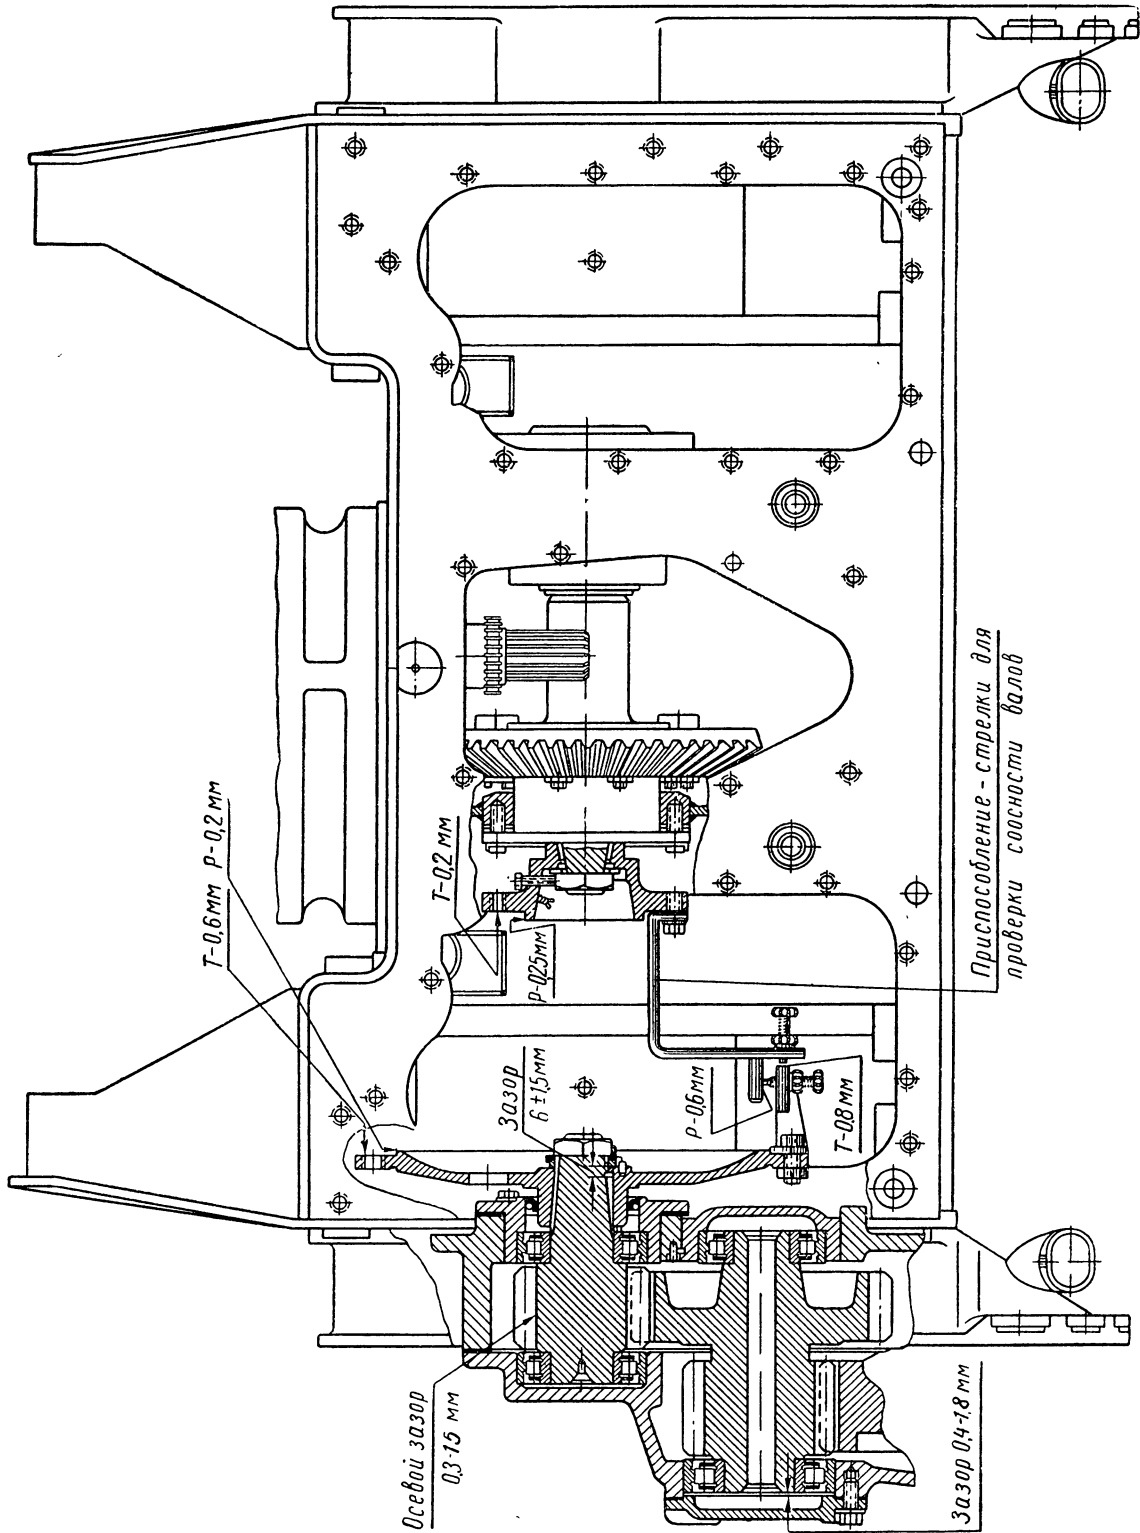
Схема проверки соосности валов бортовых фрикционов и ведущей шестерни бортового редуктора.
